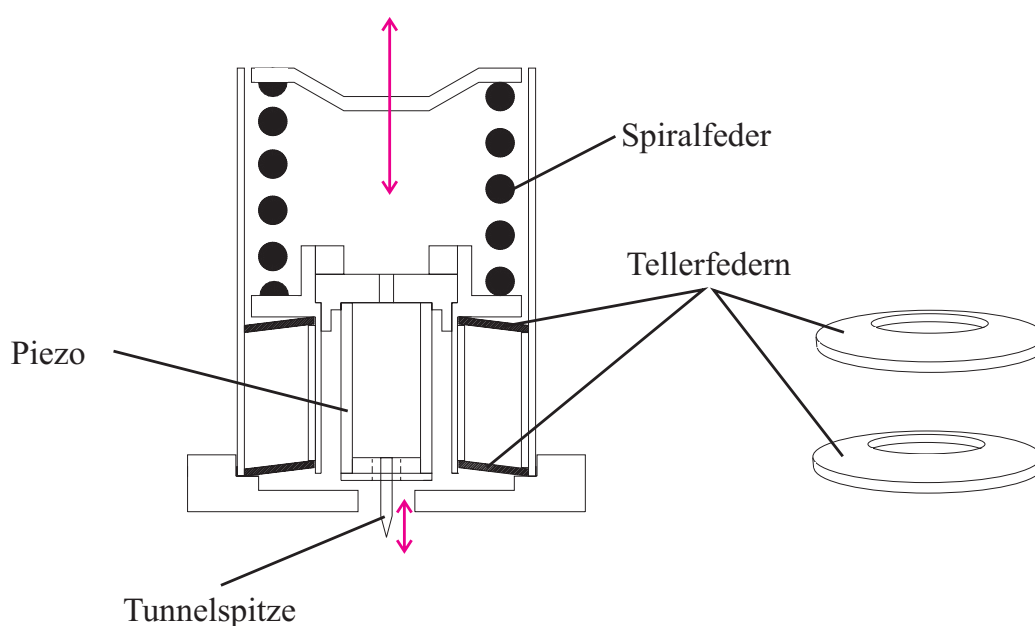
Skizze des STM-Feintriebs: Die Einstellschraube (nicht gezeigt) drückt auf ein System bestehend aus einer Spiralfeder und zwei Tellerfedern.
